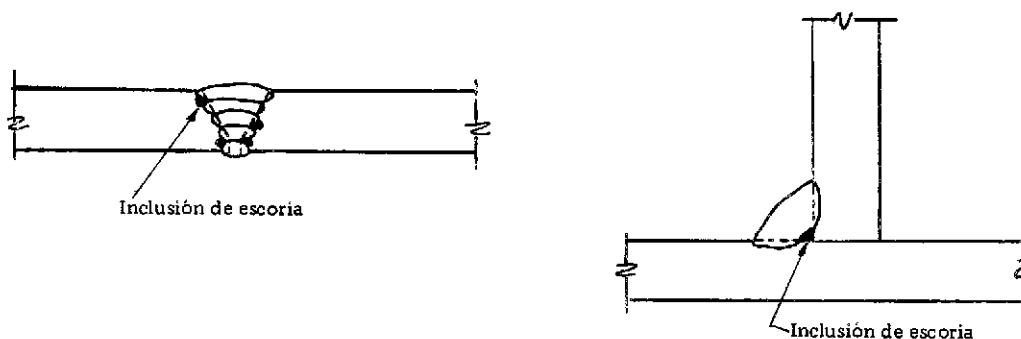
Inclusiones de escoria en juntas soldadas.
